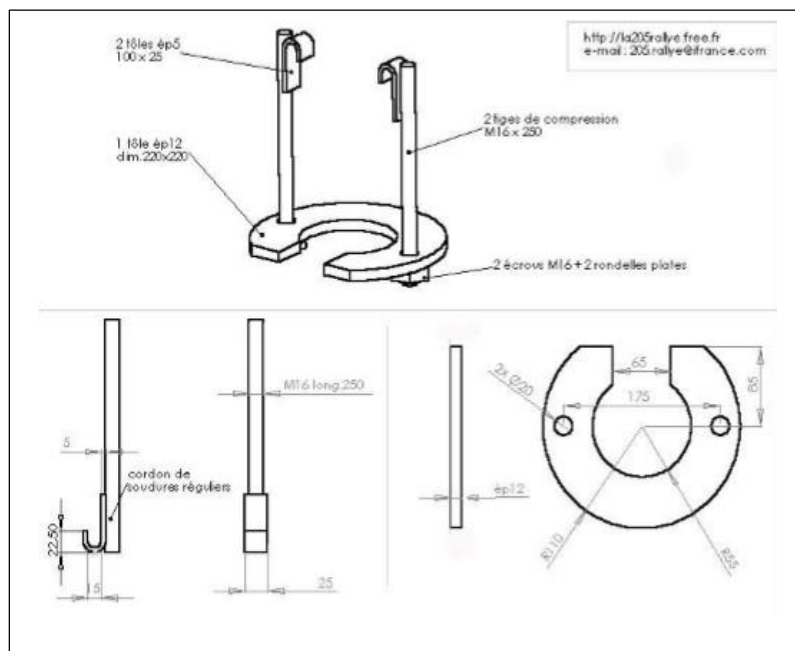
vue d'ensemble éclatée du compresseur à deux tiges de compression [10]
